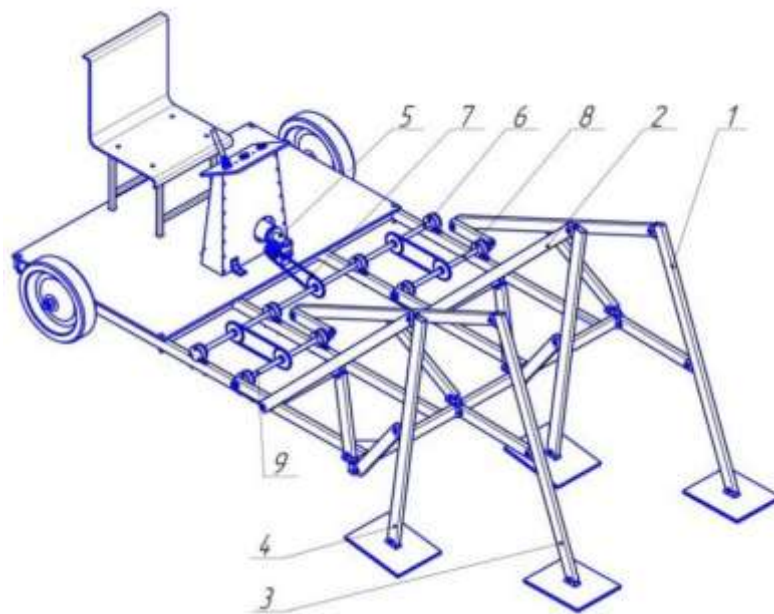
Конструкція транспортного пристрою Чебишева:
